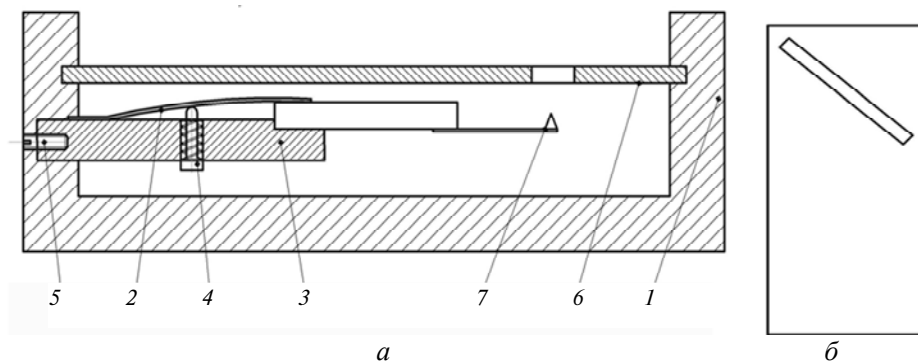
Схематичне зображення тримача для зондів (а): 1 – корпус тримача; 2 – жорстка пластина; 3 – столик; 4 – кнопка відхилення жорсткої пластини; 5 – шпилька; 6 – маска, вид згори (б); 7 – чутливий елемент АСМ.
